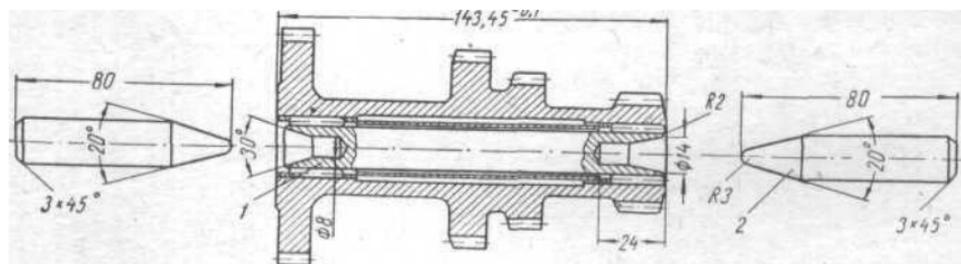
Оправки для выпрессовывания и запрессовывания оси блока шестерен промежуточного вала
